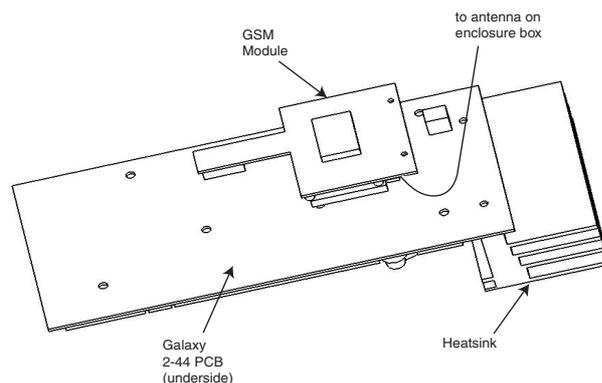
Modulo GSM collocato al di sotto della PCB Galaxy 2-44
